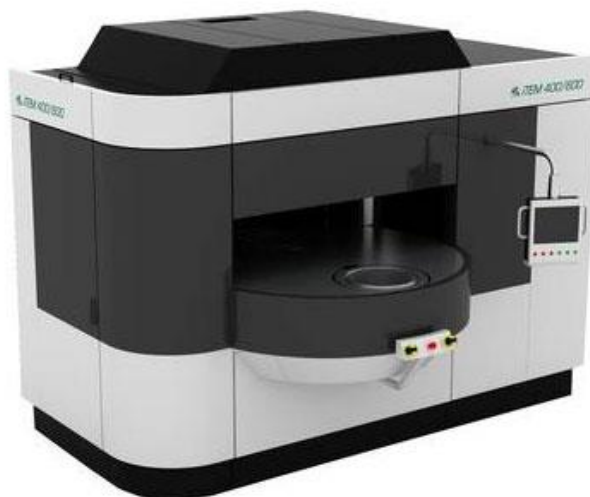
Общий вид станка по удалению заусенцев ITEM 400 – 600
